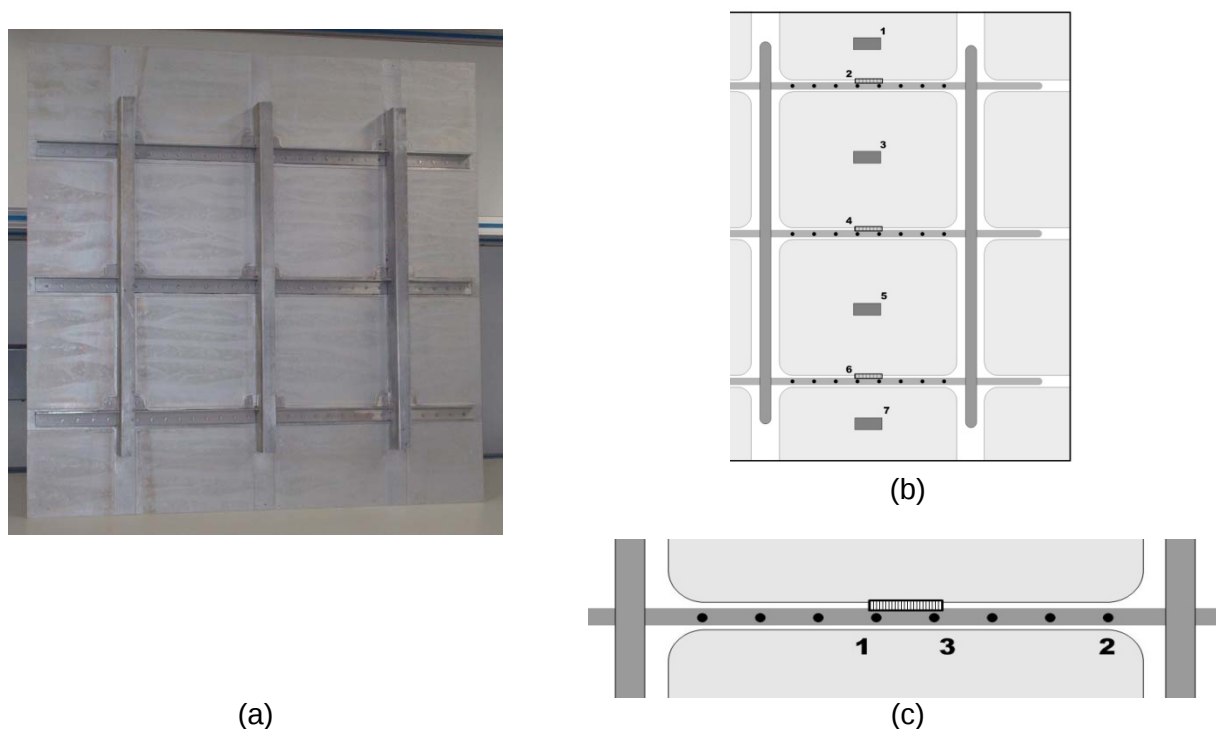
(a) Componente aeronáutico utilizado. (b) Posições dos sensores colados à estrutura. (c) Vista detalhada dos rebites a serem retirados.
